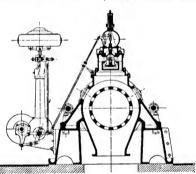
Zwangläufig gesteuertes Rücklaufventil, Patent König der Ascherslebener Maschinenbau-Aktiengesellschaft.
